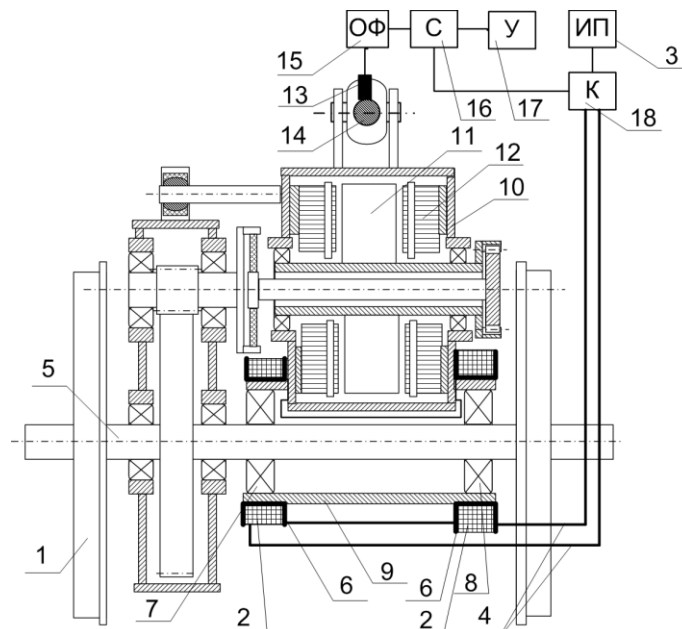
Конструкция тягового привода с электромагнитным усилителем сцепления: 1—колесная пара; 2—катушка; 3—источник питания; 4—провод; 5—ось; 6—каркас; 7,8—подшипник качения; 9— труба; 10—тяговый электродвигатель; 11—ротор; 12—статор; 13—датчик продольного усилия; 14—тяга подвески; 15— осредняющий фильтр; 16—сумматор; 17—блок уставки; 18—ключ
